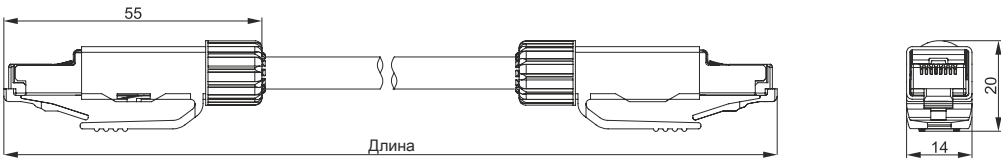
5CASP3.xxxx-00 — Размеры
